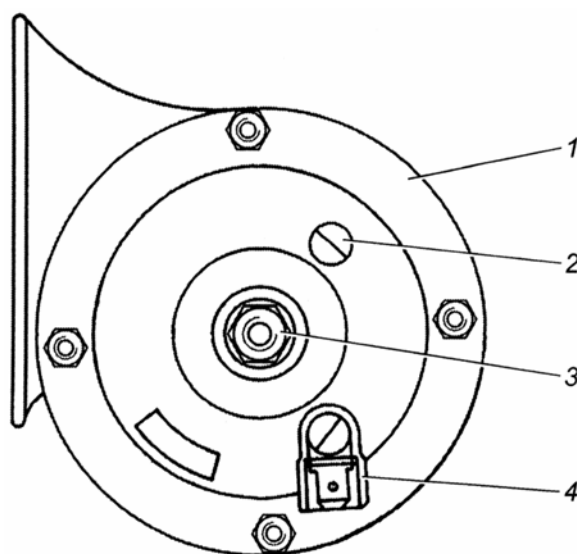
Звуковой сигнал: 1 - корпус; 2 - регулировочный винт; 3 - гайка; 4 - клемма
